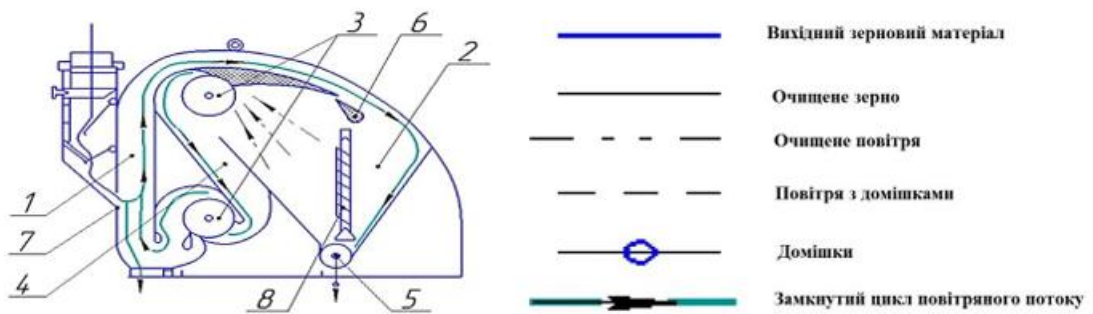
Принципова схема апарату первинної очистки Р1БДЗ - 50: 1 – пневматично сепараційний канал; 2 – камера осадження; 3 – діаметральний вентилятор; 4 – канал рециркуляції; 5 – шнек; 6 – поворотний клапан; 7 – напрямна пластина; 8 – жалюзі.
